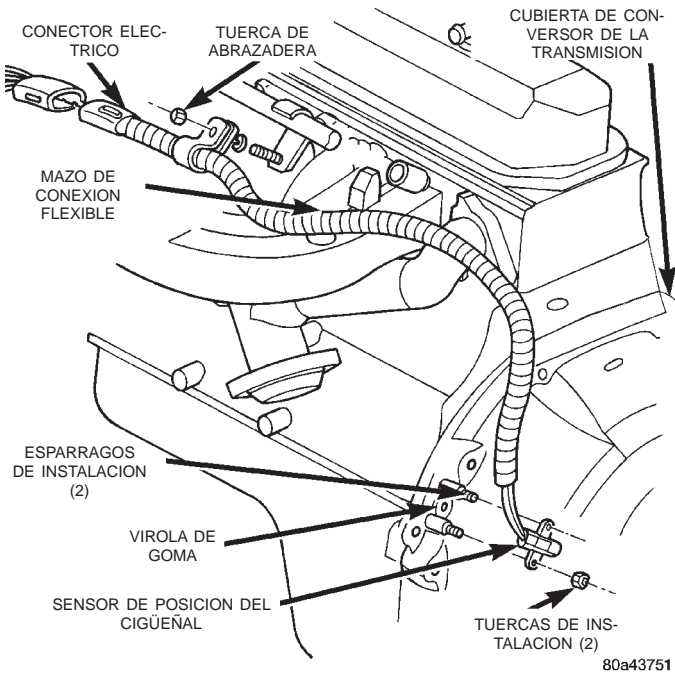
Sensor de posición del cigüeñal—Motor 2.5L
